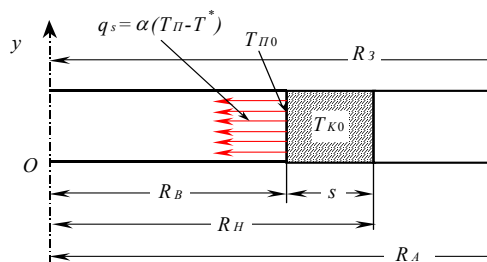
Расчетная схема процесса формирования биметаллической заготовки
